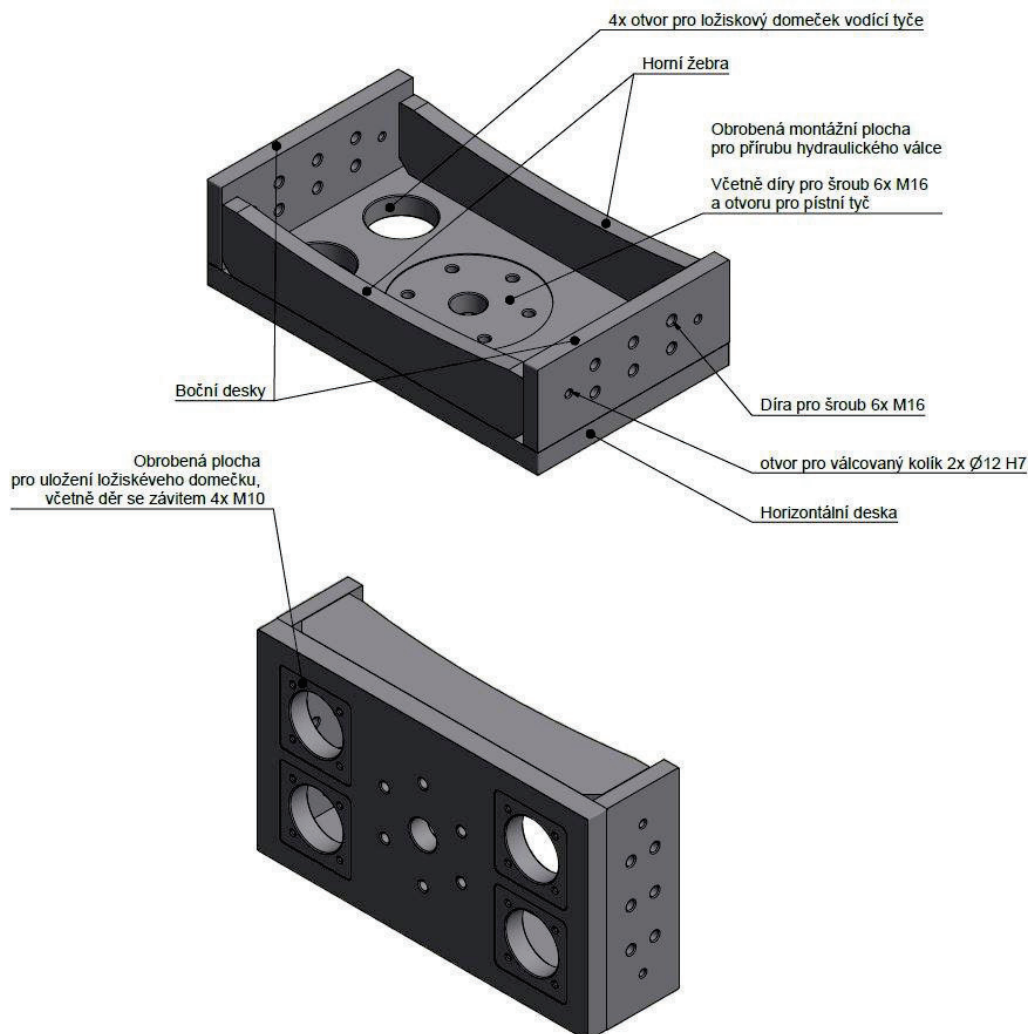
Posuvný mechanismus (vlastní zpracování)
